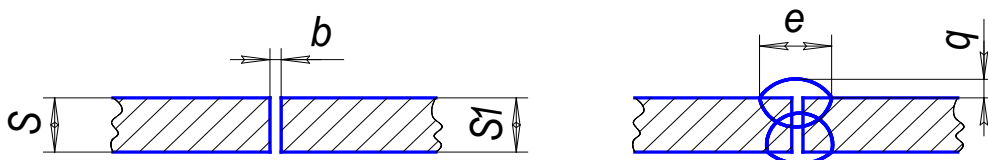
Сварное соединение С7 ГОСТ 8713-79 для сварки продольного шва
